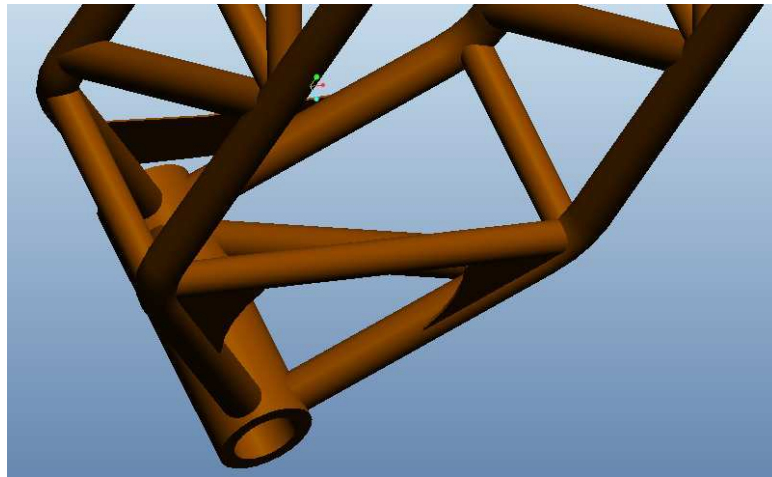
Prototipo A con refuerzos en la columna y el travesaño
